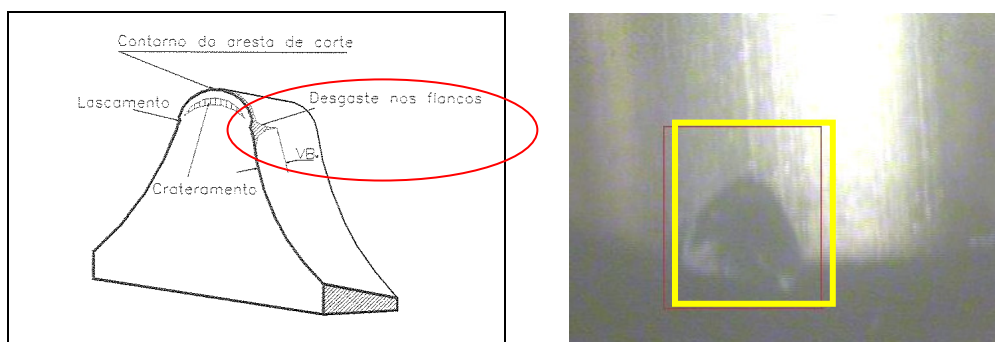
Desgaste de flanco VB no dente da ferramenta caracol
